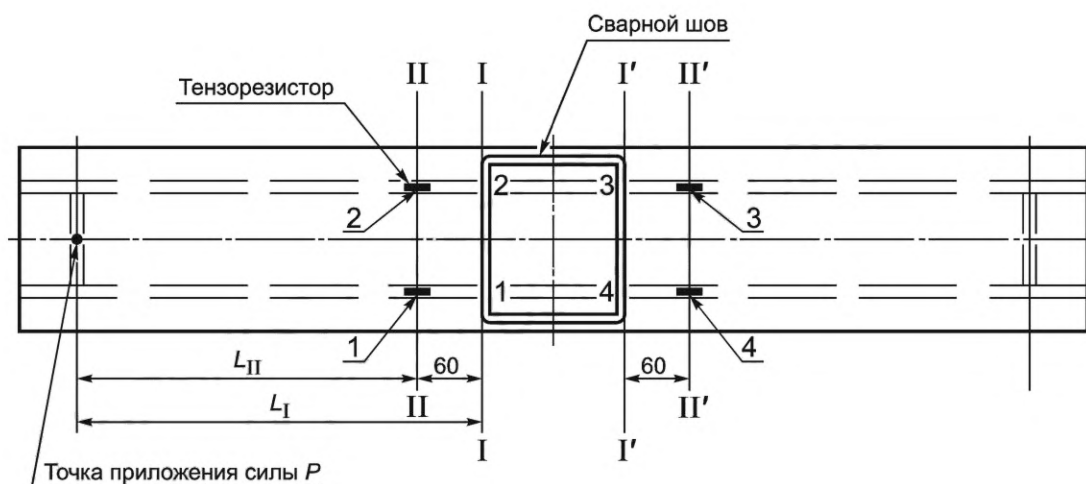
Схема установки тензорезисторов на типовом сварном образце (вид на образец сверху)
